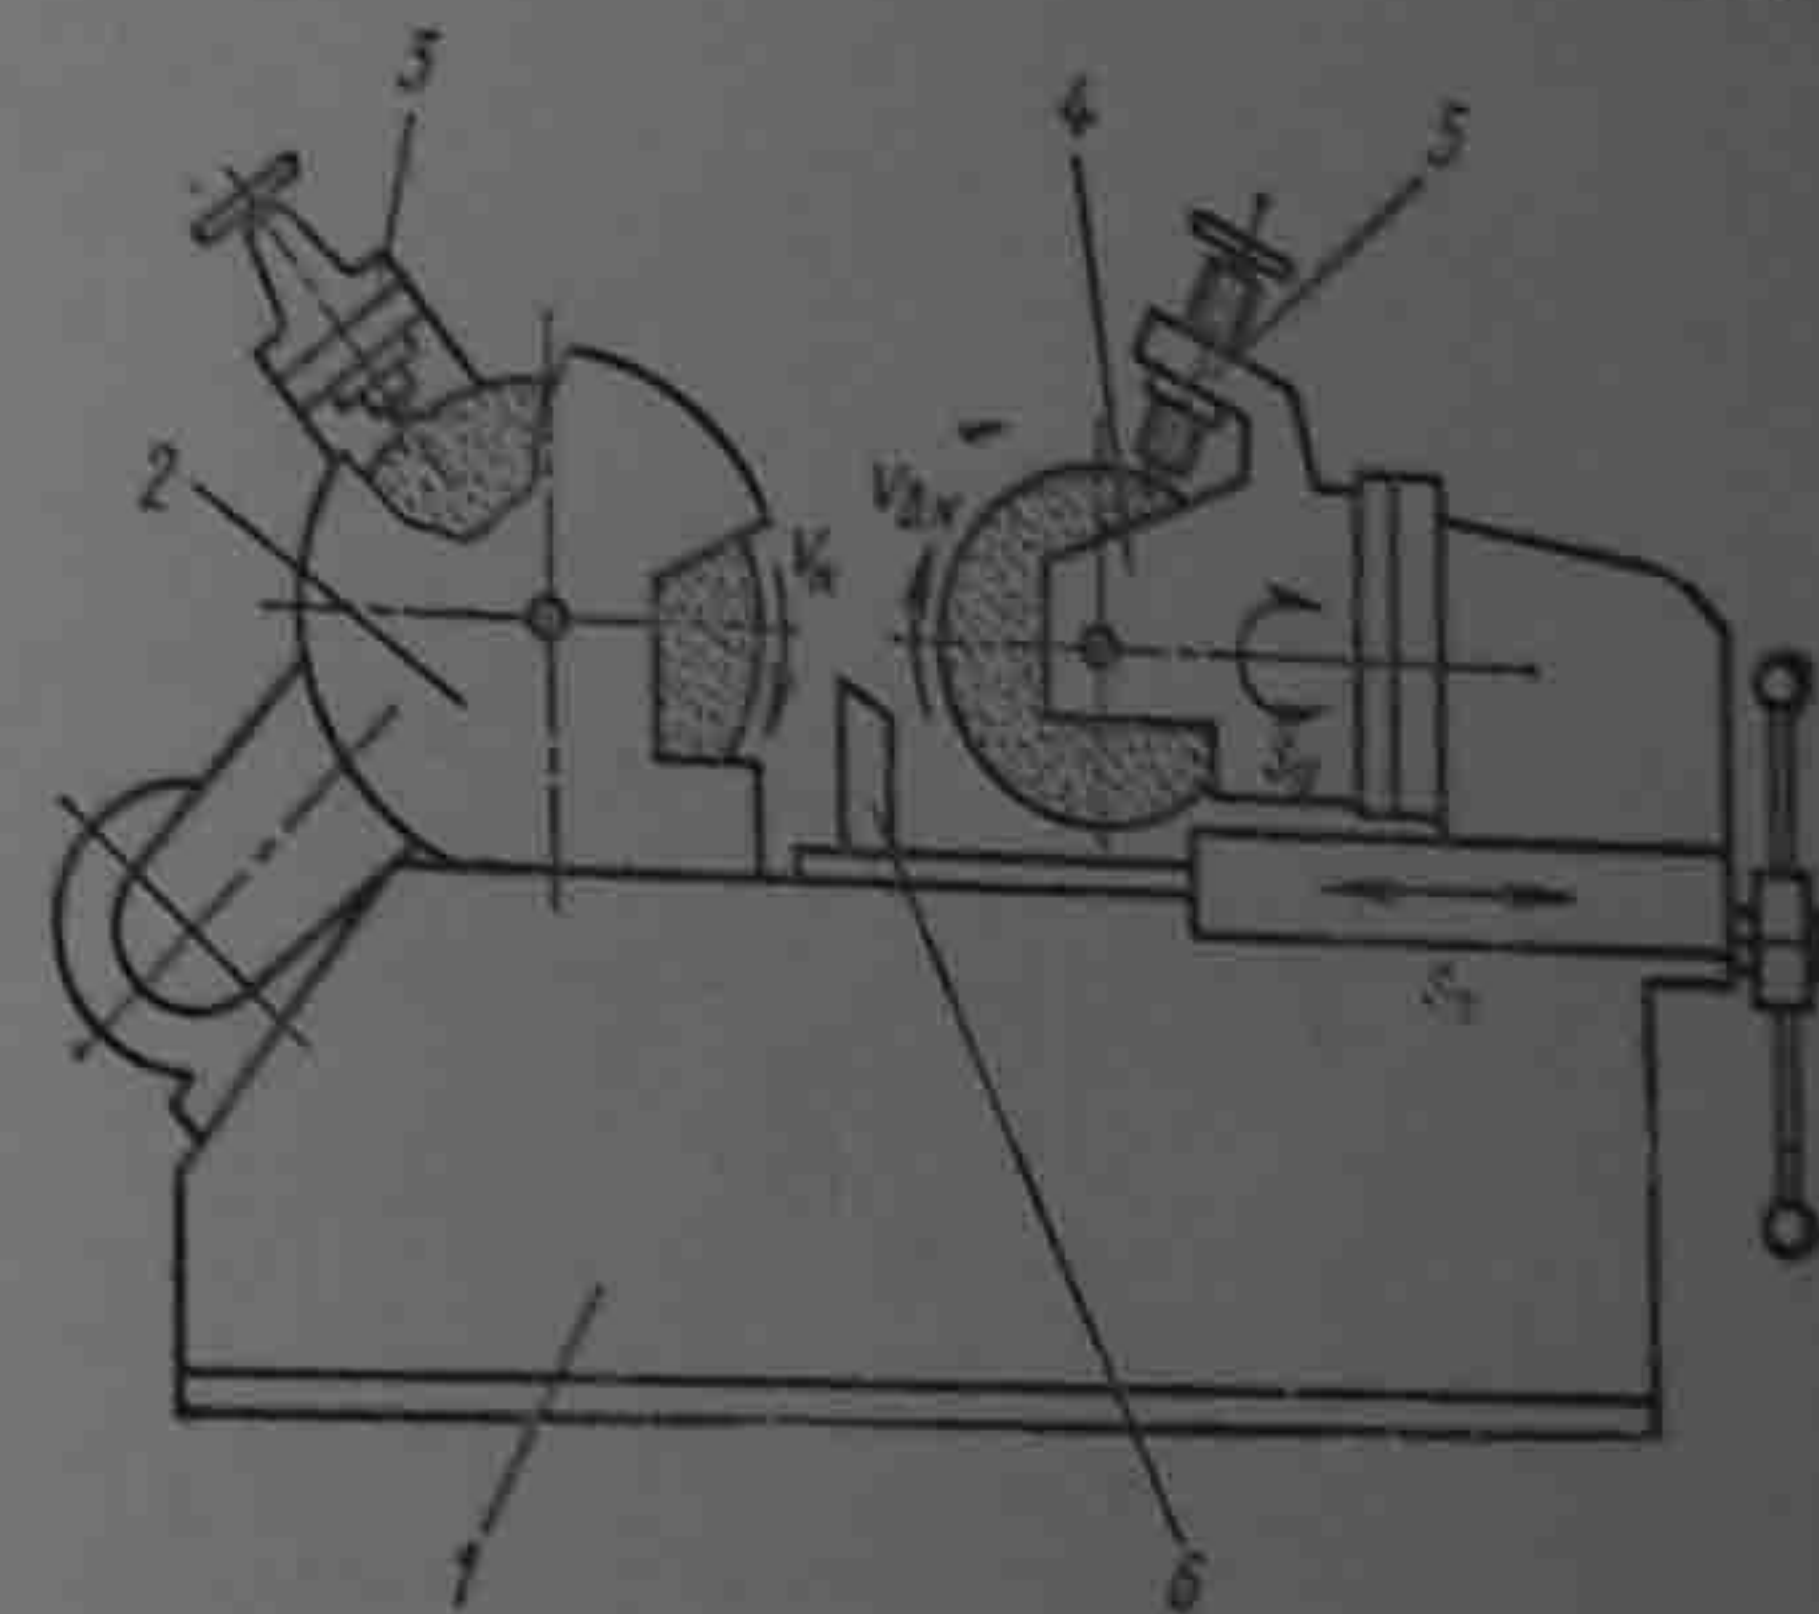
Общий вид бесцентрово-шлифовального станка
